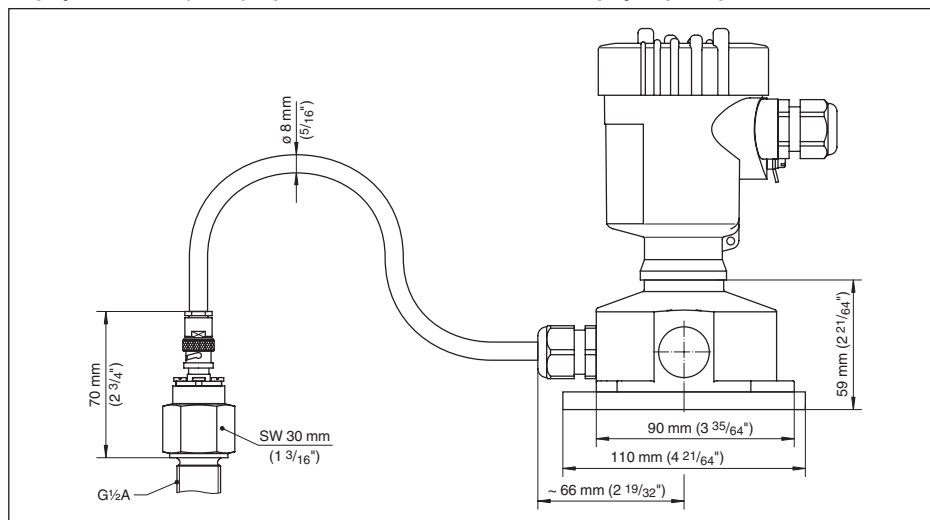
Корпус датчика - IP 54 и выносной корпус прибора
